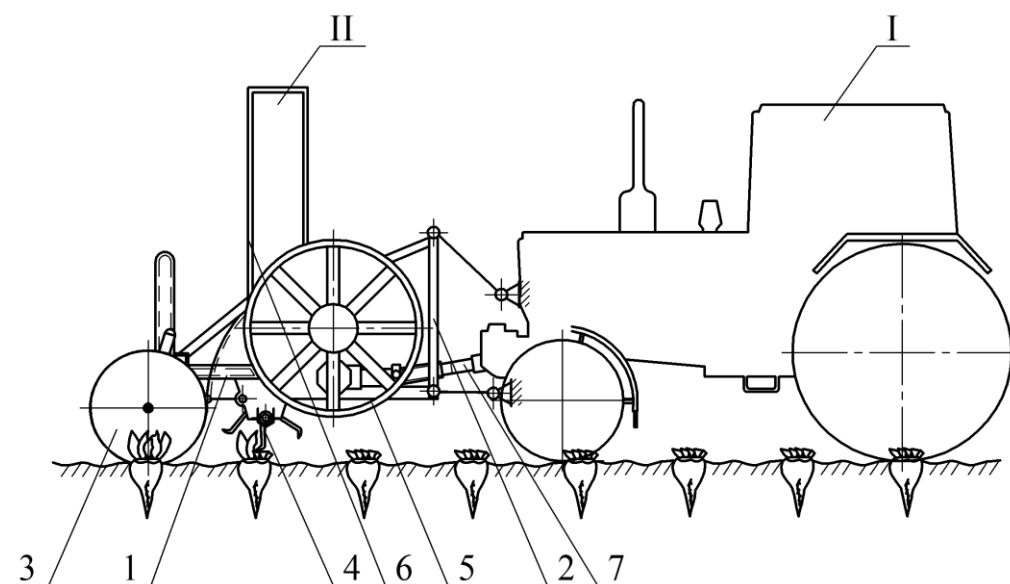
Схема гичкозбирального агрегату: 1 – рама; 2 – начіпний пристрій; 3 – опорне колесо; 4 – роторний ріжучий пристрій; 5 – транспортуючий робочий орган; 6 – завантажуючий пристрій; 7 – привід
